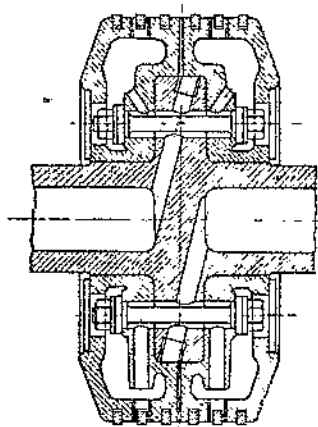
Поршневая гайка газового двигателя Е. и С.
